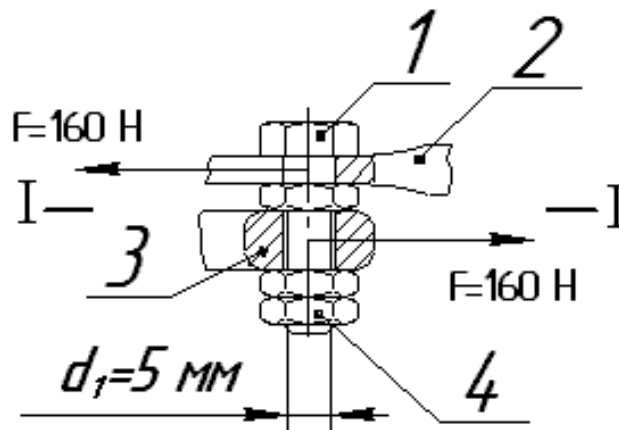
Схема нагружения болта, поперечной силой: 1-болт; 2-рычаг; 3-плечо натяжного ролика; 4-гайка
